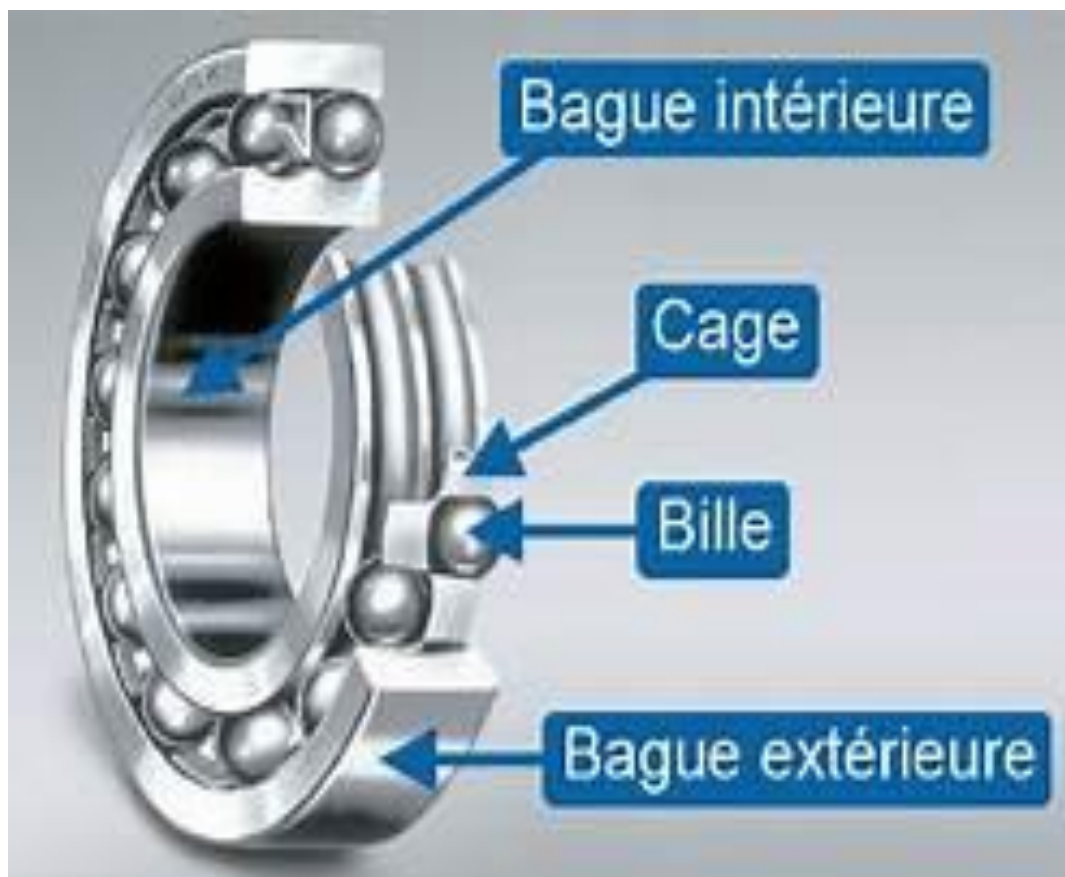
Vue éclatée des éléments constitutifs d'un roulement à billes
